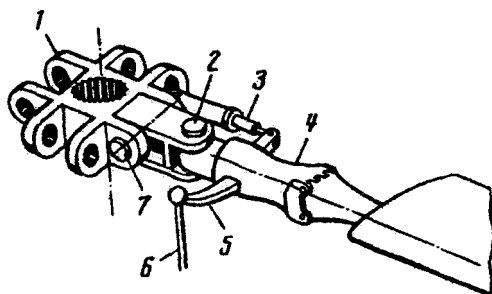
Схема втулки НВ вертолётa: 1 – корпус втулки; 2 – вертикальный шарнир; 3 – демпфер; 4 – осевой шарнир; 5 – рычаг осевого шарнира; 6 – тяга управления углами установки лопастей; 7 – горизонтальный шарнир; 8 – лопасть
